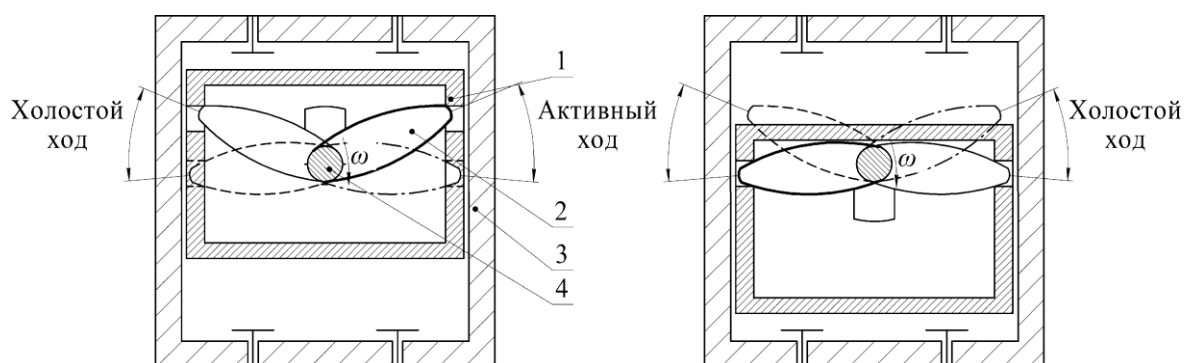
Кинематическая схема ДВС Лapidуса: 1 – поршень; 2 – кулачок; 3 – цилиндр; 4 – грузовой вал
